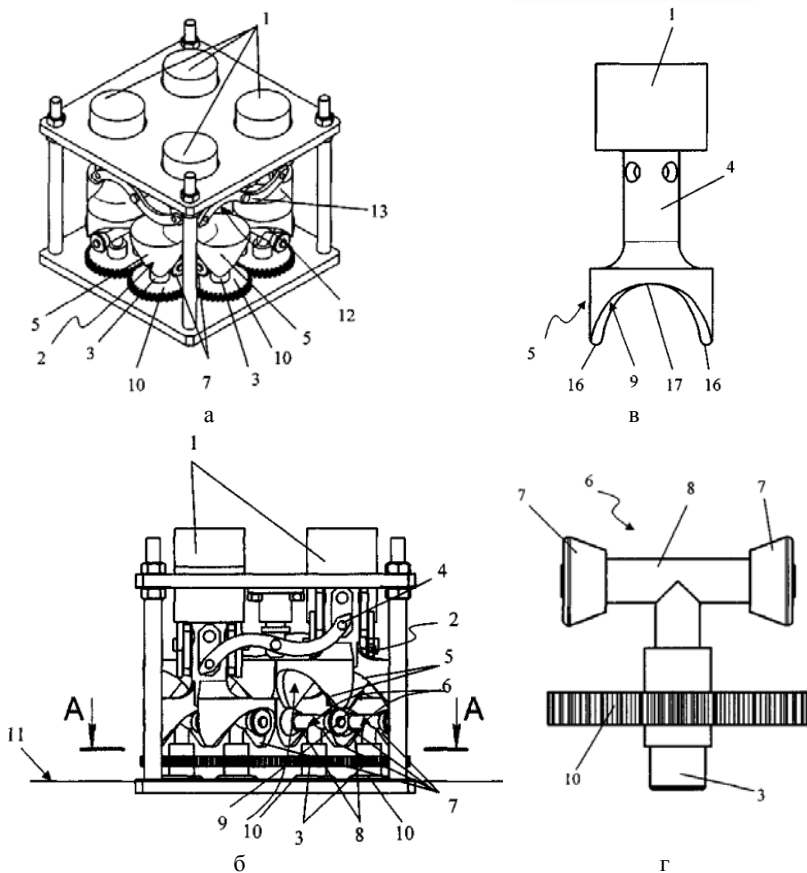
Схема конструкции двигателя с тангенциальным механизмом:
